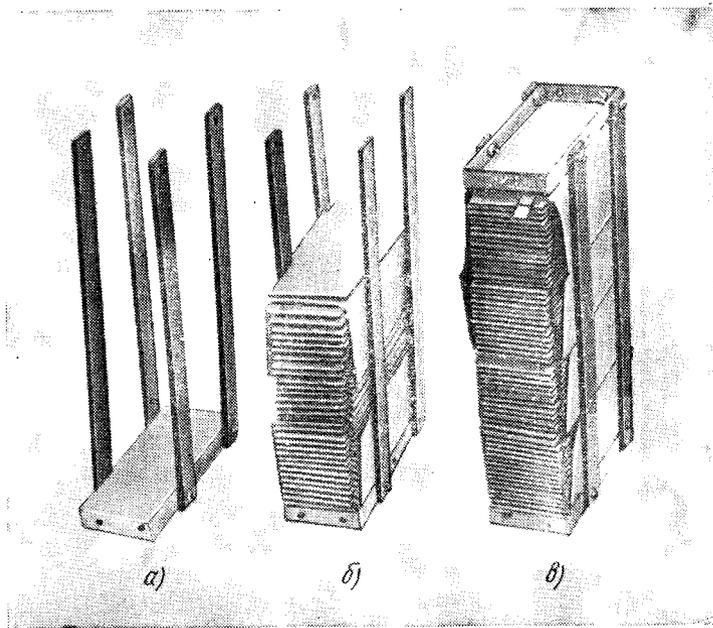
Сборка пакетов конденсатора СМ166/√3-14У1:
